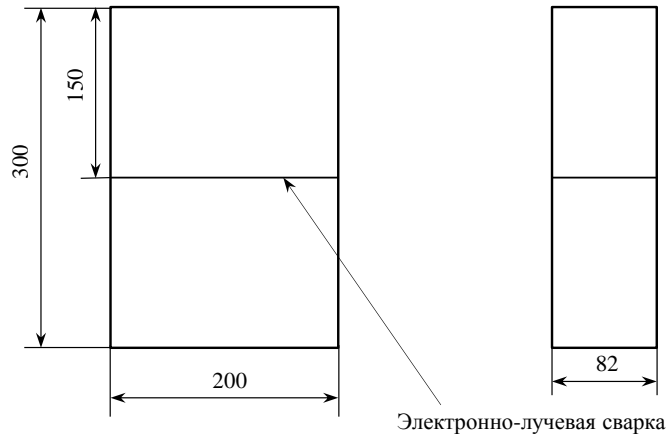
Эскиз образца под сварку, выполненного из титанового сплава ВТ6ч., толщиной 82 мм
